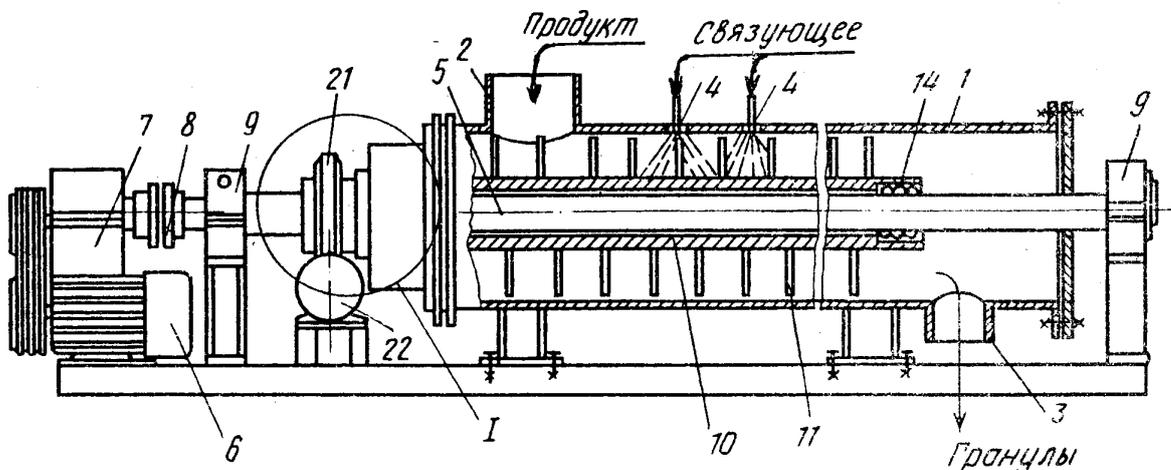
Гранулятор сыпучих материалов: 1 – цилиндрический корпус; 2 – штуцер для загрузки продукта; 3 – штуцер для разгрузки продукта; 4 – форсунки; 5 – центральный вал; 6 – электродвигатель; 7 – редуктор; 8 – муфта; 9 – подшипниковые узлы; 10 – полый вал; 11 – штифты; 12, 13 – продольные канавки; 14 – шарики; 15 – упорный подшипник; 16 – втулка; 17 – палец; 18 – паз; 19 – втулка; 20 – подшипник; 21 – червячное колесо; 22 – реверсивный электродвигатель; 23 – червяк
